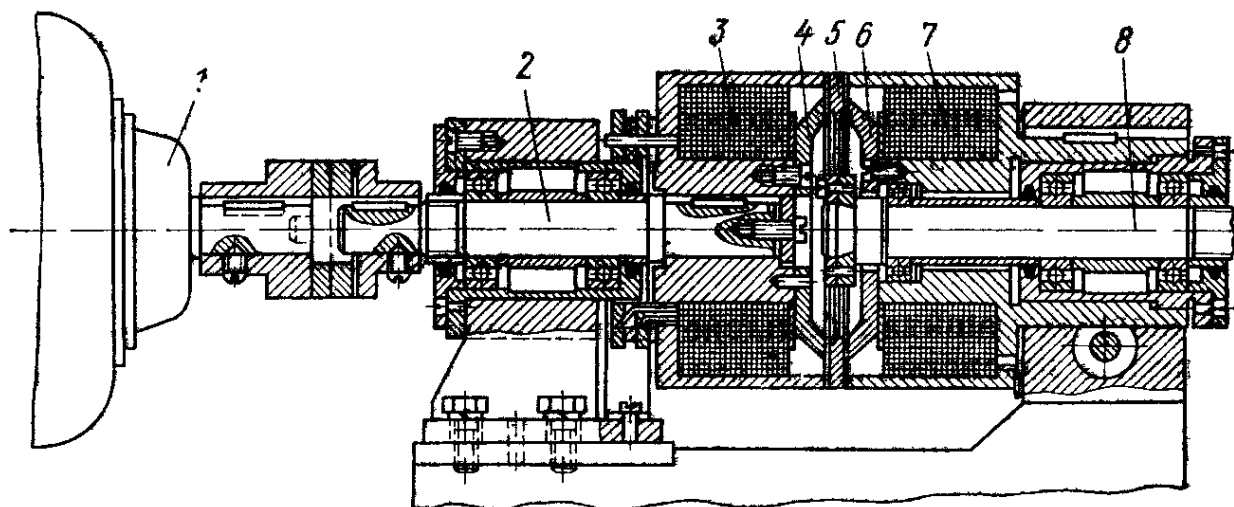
Электромагнитная муфта привода шагового перемещения с двигателем:
